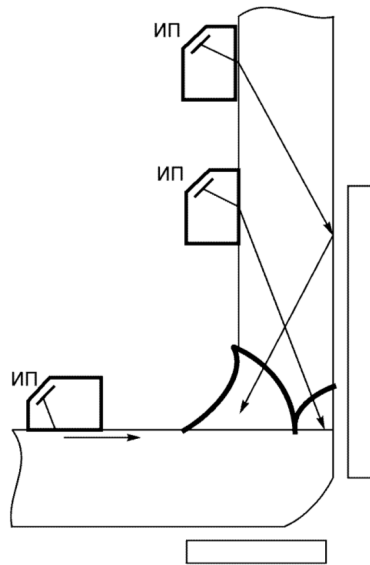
Схема прозвучивания углового сварного соединения при одностороннем доступе совмещенными наклонными и прямыми преобразователями, преобразователями подповерхностных (головных) волн
